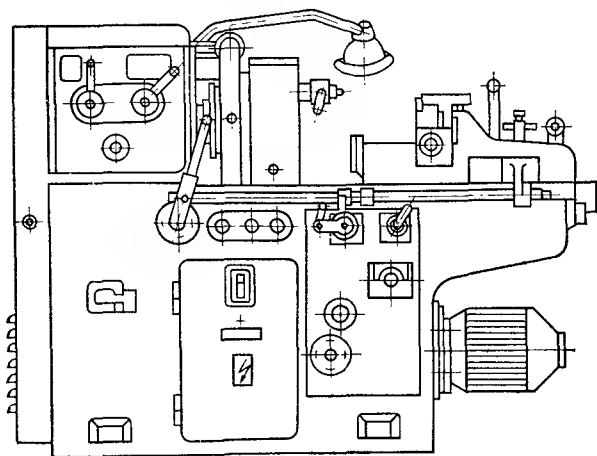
Полуавтомат резьбонарезной 5Д07
